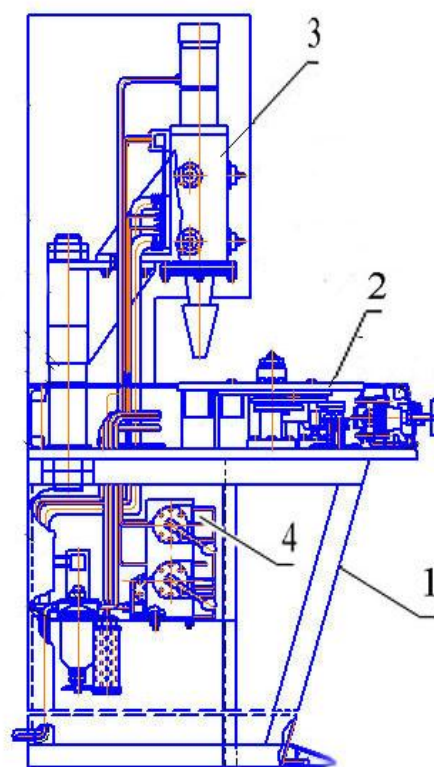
Общий вид и схема установки для сварки изделий из полистирола УСМ-11
